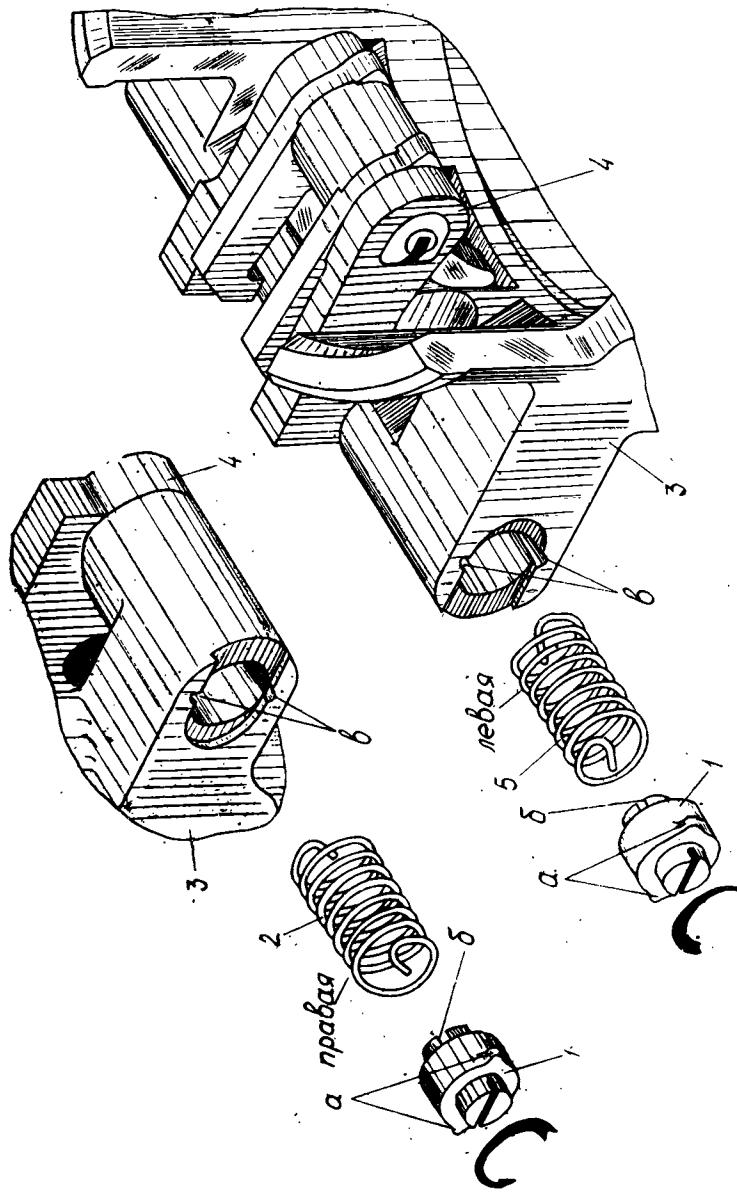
Установка пружин лопаток предохранителя 04 Сп:
